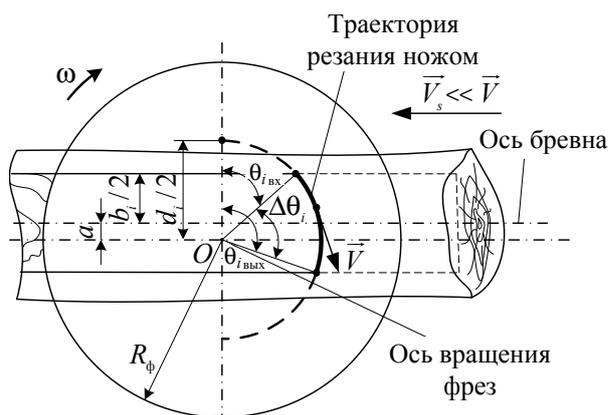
Общая схема обработки бревен на фрезерно-брусующем станке
